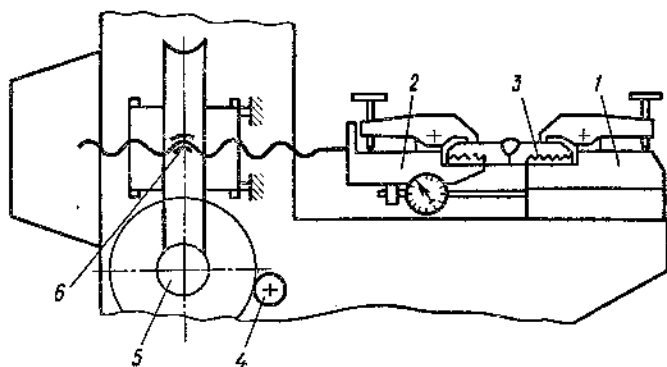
Схема машины ЛТП-6 для испытаний на холодные трещины при сварке:
